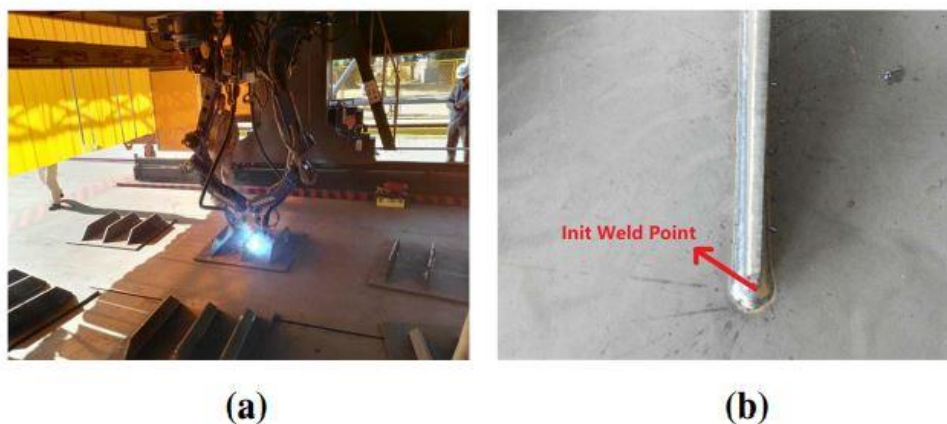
a) Processo de Soldadura. B) Resultado final da soldadura. Adaptado de (Yang *et al.*, 2020).
